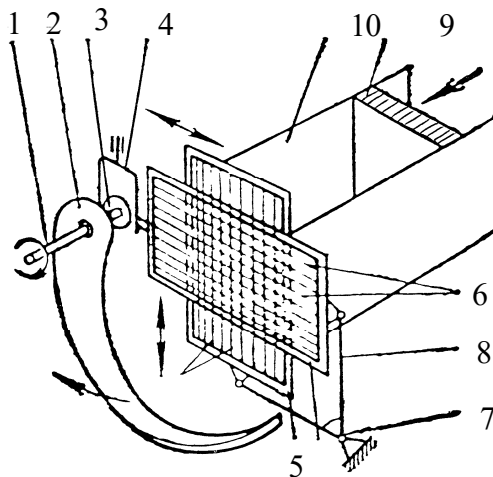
Шпигорізка. Принципова схема різального вузла: 1 – приводний вал; 2 – серпоподібний ніж; 3 – ексцентрик; 4 – вилка; 5 – ножові рамки; 6 – пластинчасті ножі; 7 – вісь; 8 – кутовий важіль; 9 – штовхальник; 10 – короб живлення
